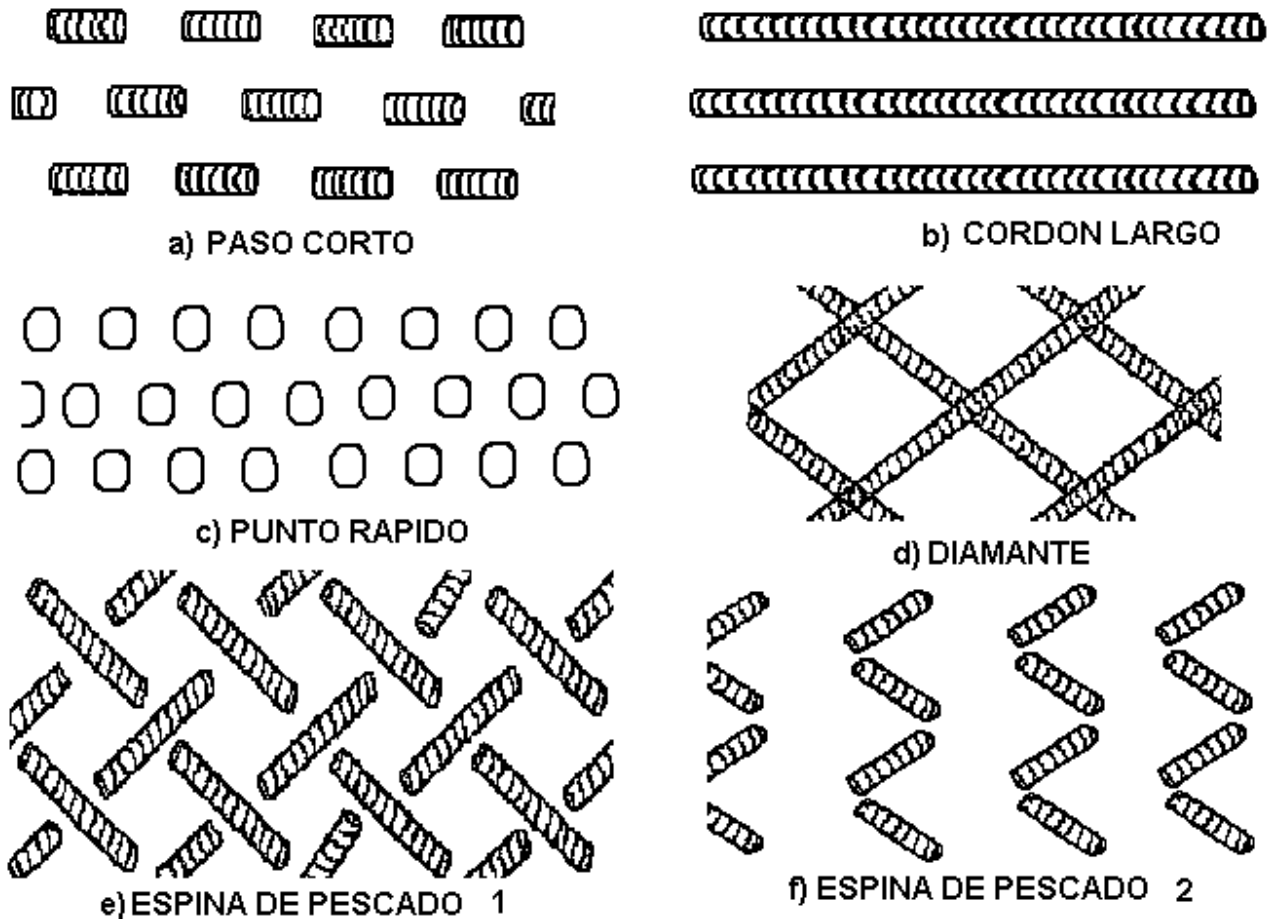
Algunos tipos de cordones de soldadura (18, 32)
